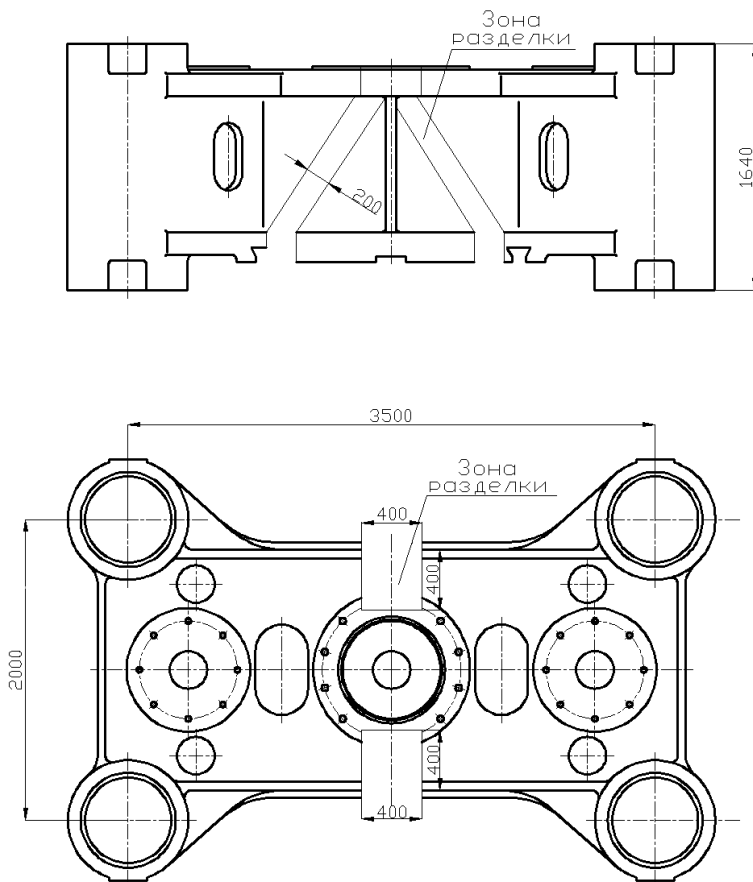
Разделка под сварку боковых стенок, верхней и нижней плит подвижной поперечины ковочного пресса силой 32 МН
